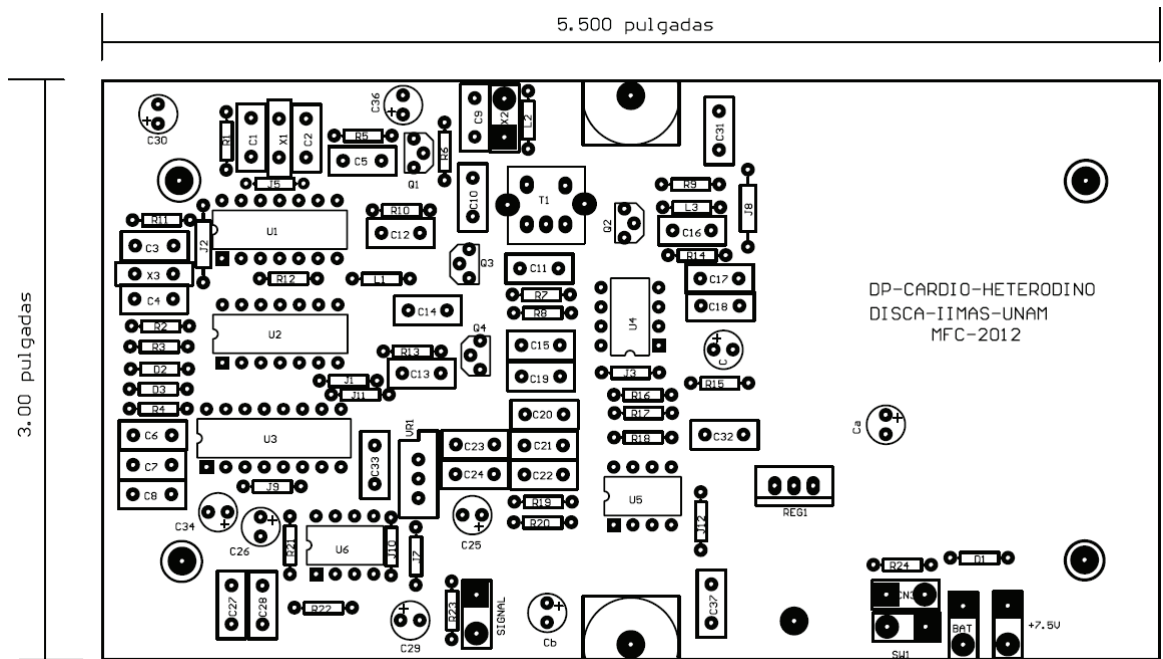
Mascarilla de componentes del circuito impreso del detector Doppler Heterodino
